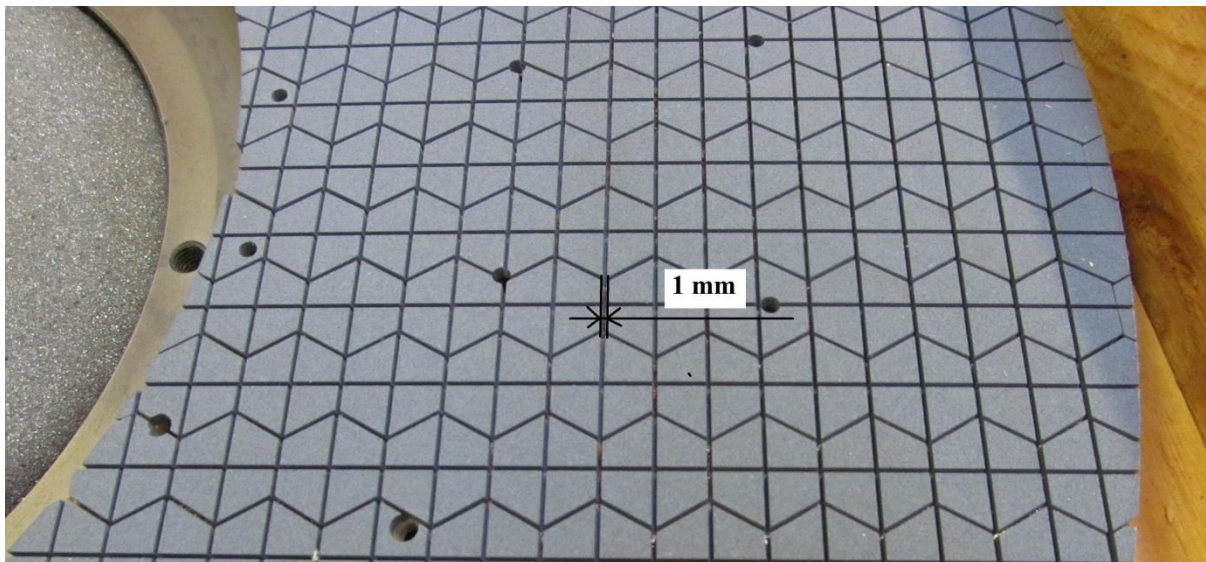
Detail starší specifikace brusných segmentů (šířka mezi segmenty 2 mm) [autor]
